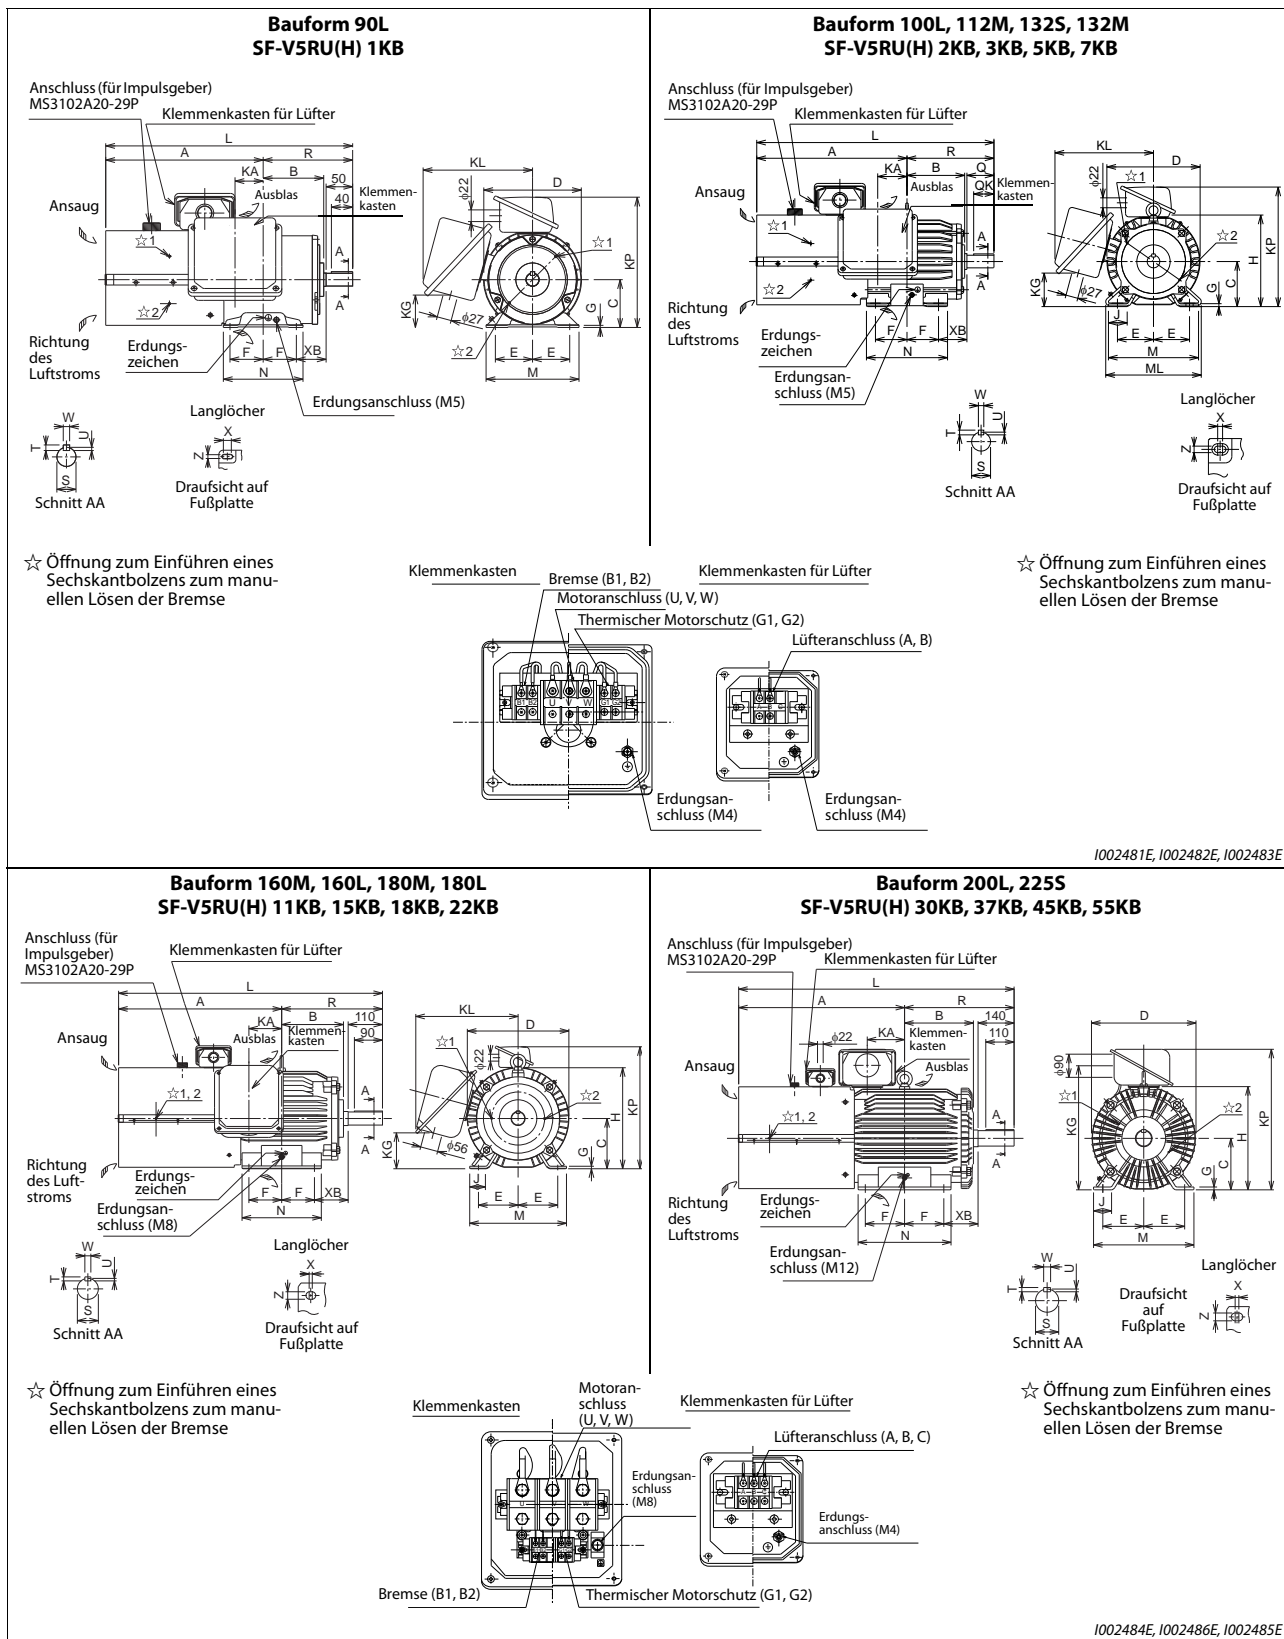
Maßzeichnungen der Motoren SF-V5RU(H) (Standardmotoren mit Bremse zur Aufstellung auf Unterbau)
